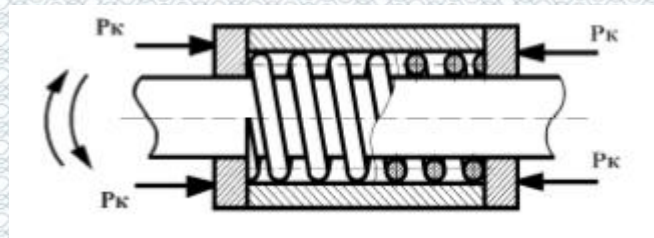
Схема підшипника з рухомих пружинним вкладишем
